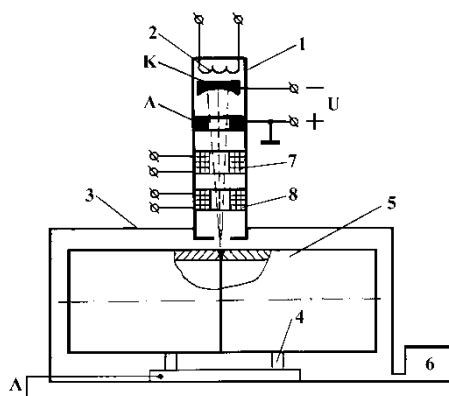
Схема установки для сварки электронным лучом:
